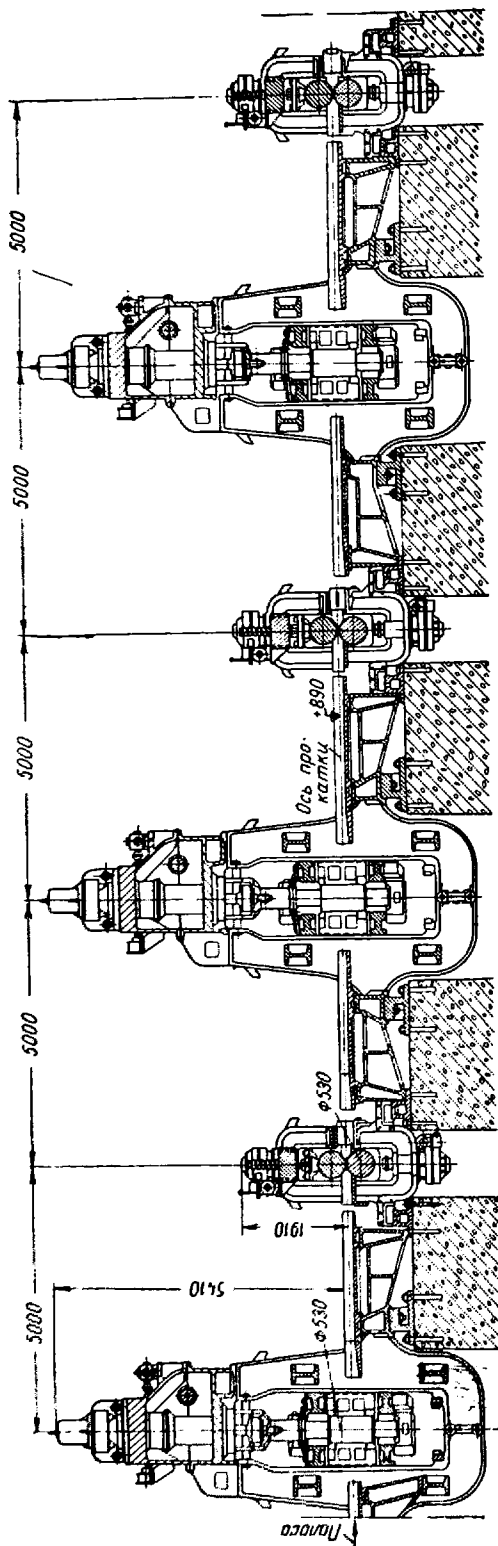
Схема расположения оборудования непрерывного заготовочного стана
